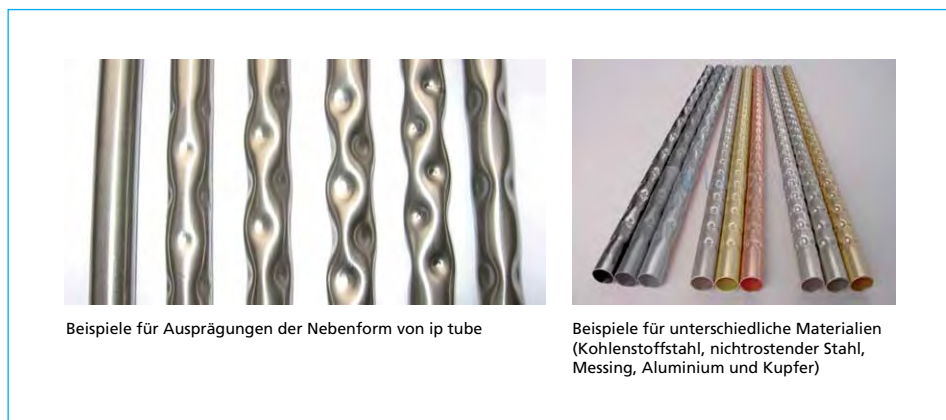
Rohre mit Nebenformen mit der Handelsbezeichnung ip tube, Hersteller La Mont GmbH, Wildau/Brandenburg
